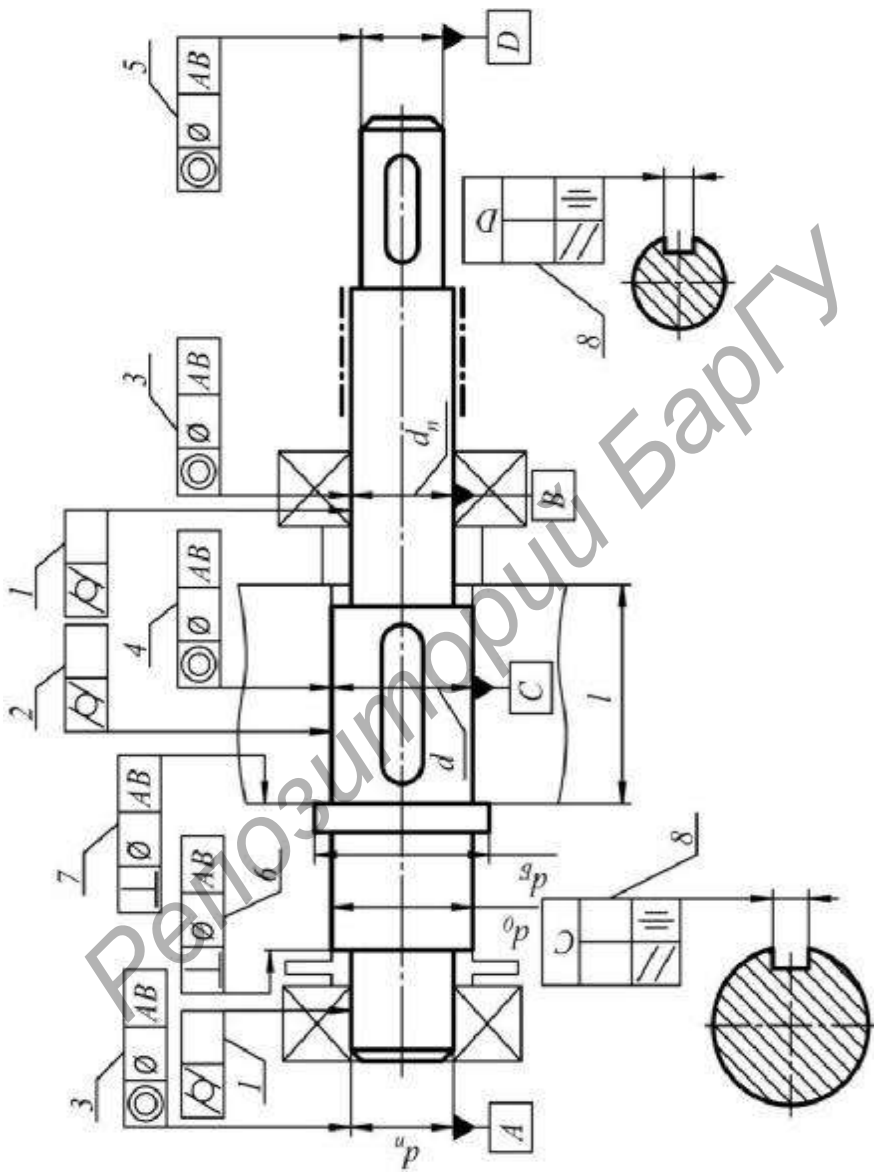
Допуски формы и расположения поверхностей
